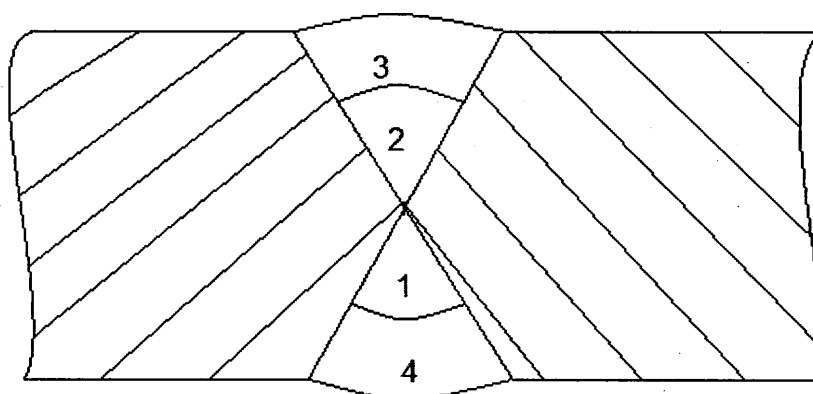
Расположение сварных валиков при сварке обечайки 1
